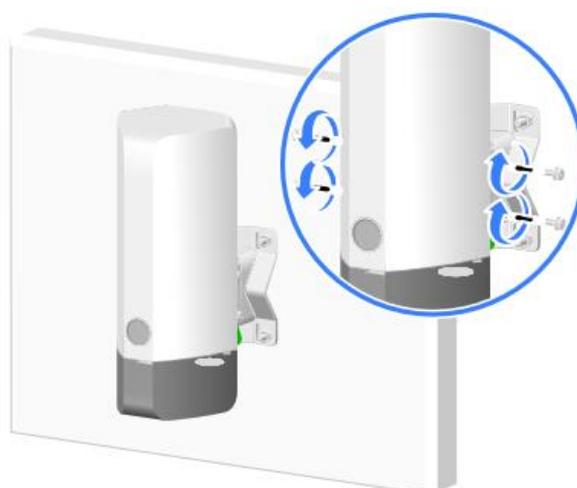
Fixação do dispositivo e cabo de aterramento
